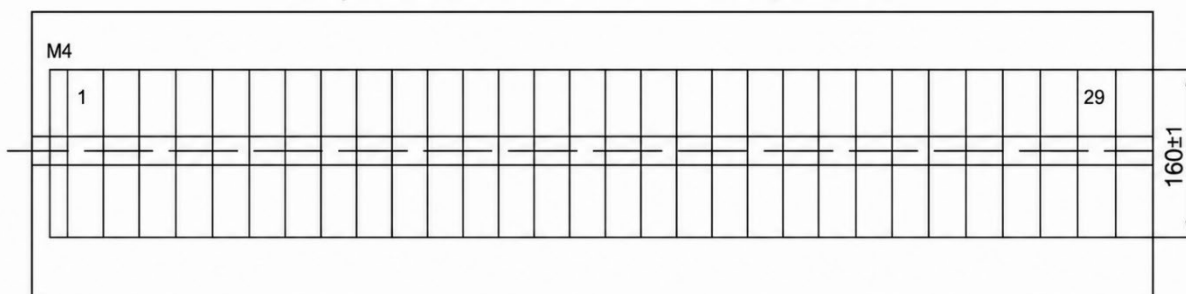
Plan sečenja, ploča 2 NM490K
